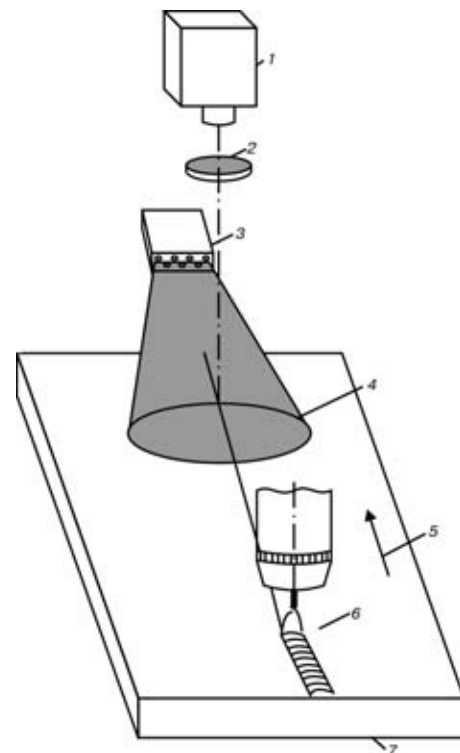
Принцип работы системы слежения за стыком с зазором, близким к нулю: 1 — ПЗС-камера; 2 — интерференционный фильтр; 3 — осветитель; 4 — рассеянный свет; 5 — направление сварки; 6 — зона сварки; 7 — изделие
